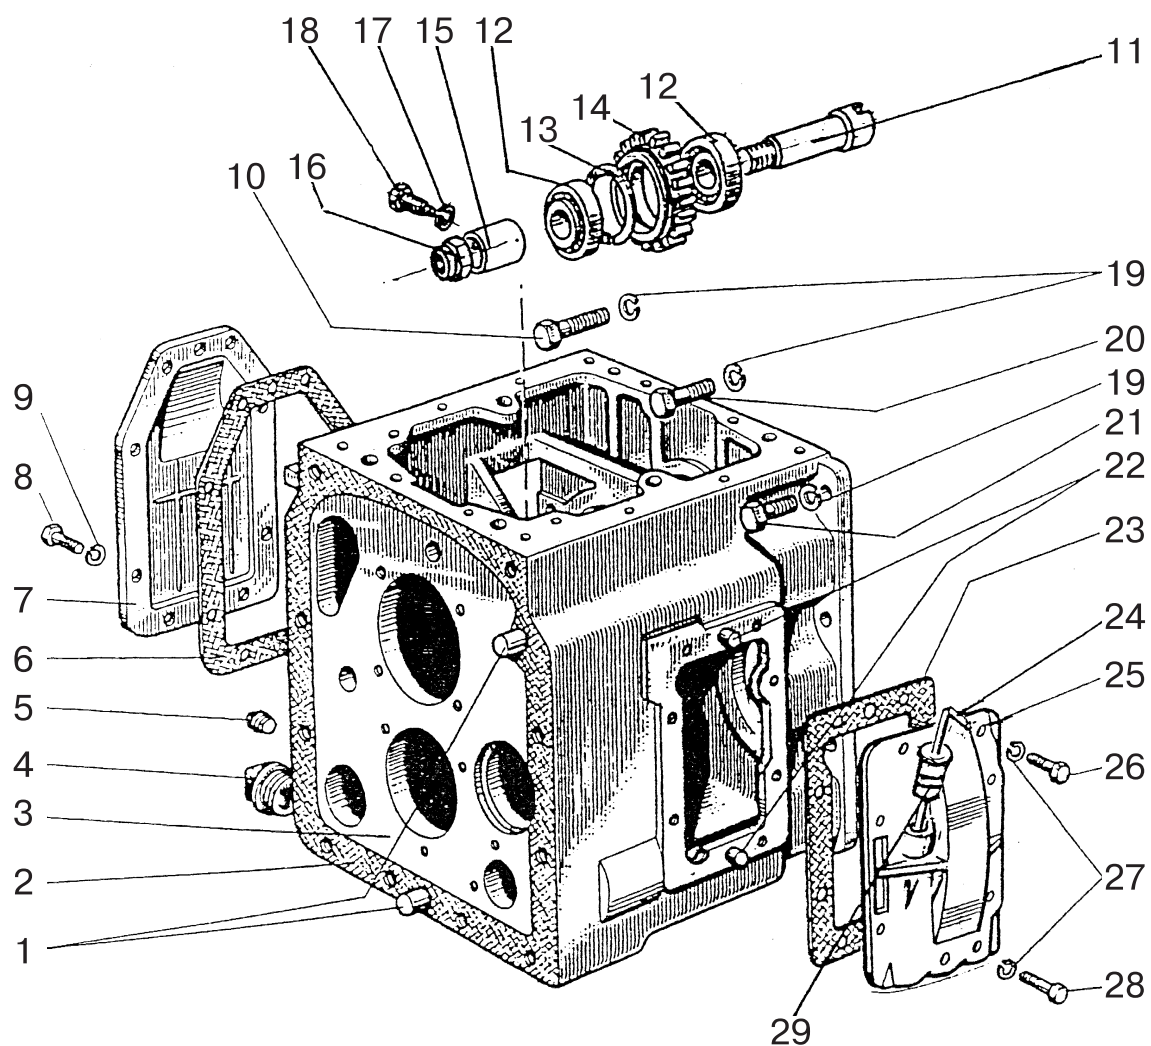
Коробка передач. Корпус. Привод ПБМ
